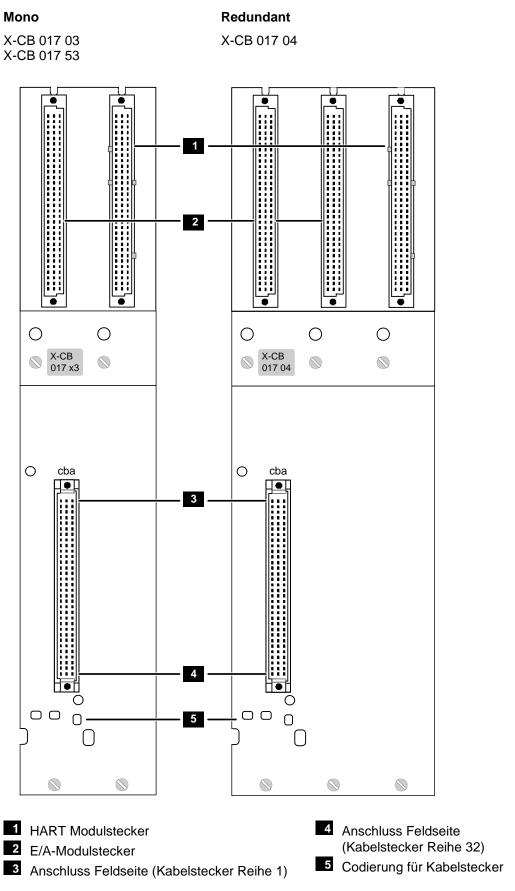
Connector Boards X-CB 017 mit Kabelstecker
